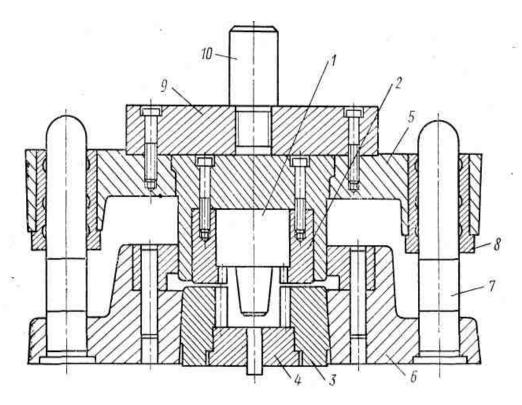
Схема конструкции штампа винтового пресс-молота для штамповки полой поковки с наружными шлицами:
